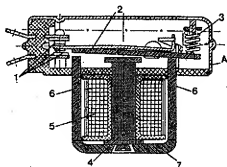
Репрокон, разработанный автором: 1 — контактные накладки; 2 — жесткий ферромагнитный якорь; 3 — возвратная пружина; 4 — сердечник, выходящий из герметичной оболочки А; 5 — катушка управления; 6 — участки магнитопровода, выходящие из герметичной оболочки А; 7 — съемный участок магнитопровода
